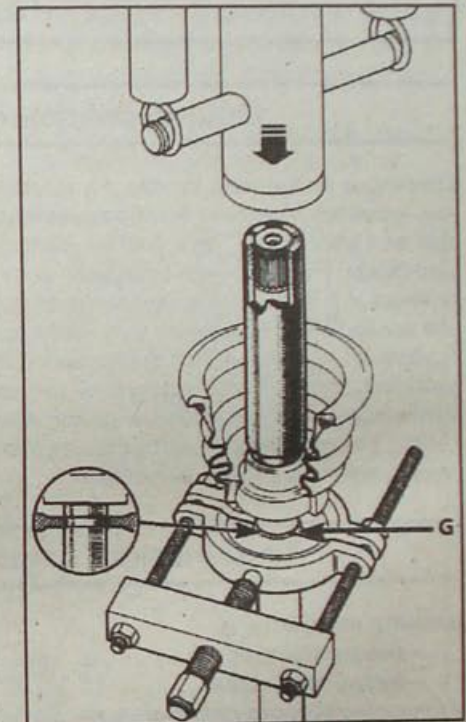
Установка эластичного гофрированного защитного чехла в сборе с подшипником на левый приводной вал:
